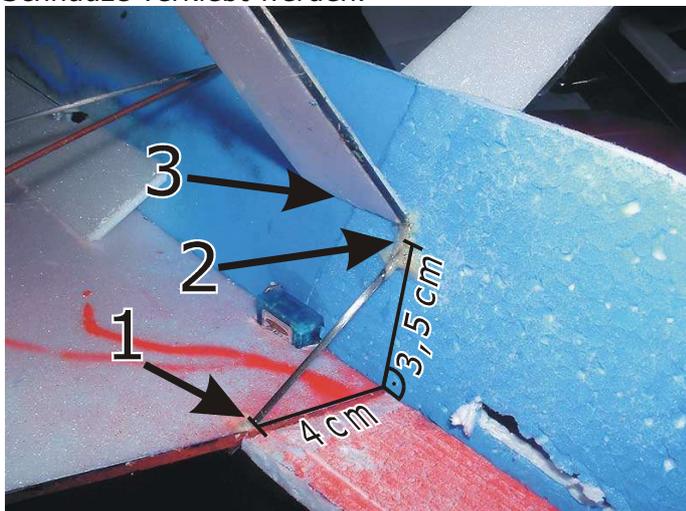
Hier sieht man die Fahrwerksposition und die Akkubefestigung.
